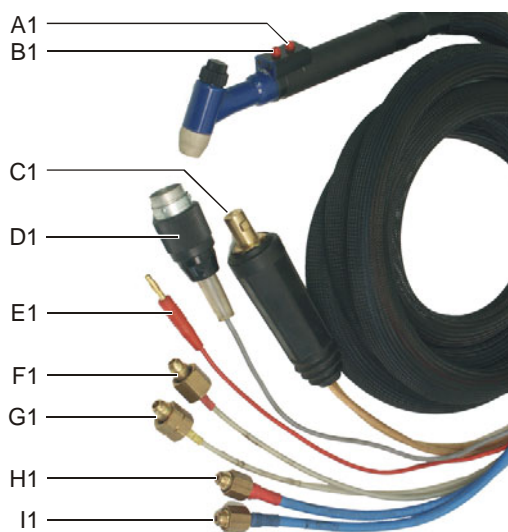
PWH 150 горелка для ручной сварки с подачей холодной проволоки
